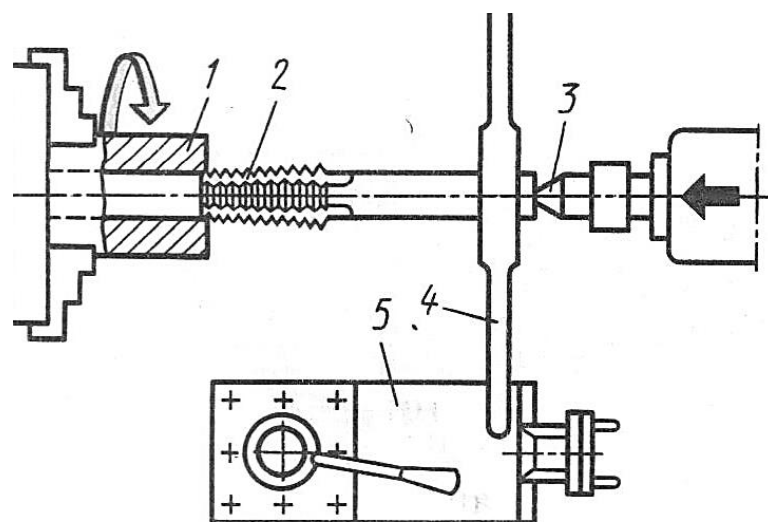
Нарезание резьбы метчиком: 1 – заготовка; 2 – метчик; 3 – центр; 4 – вороток; 5 – верхний суппорт
